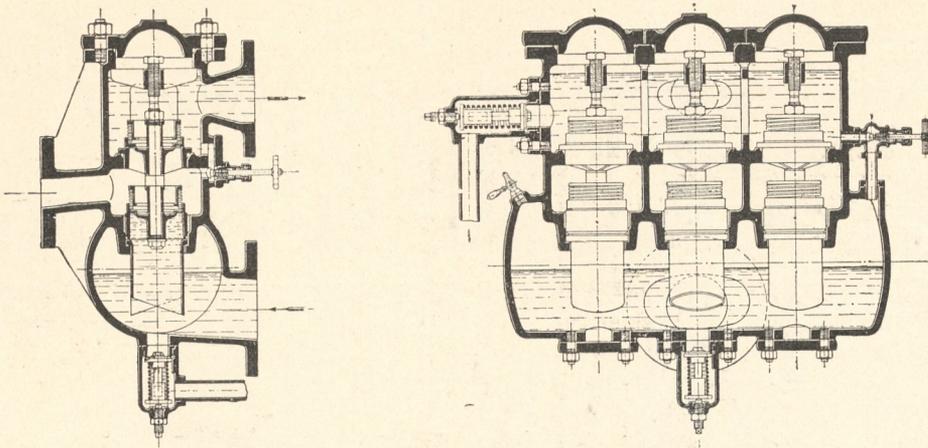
Saug- und Druckventilkasten zur Drillingspumpe.
